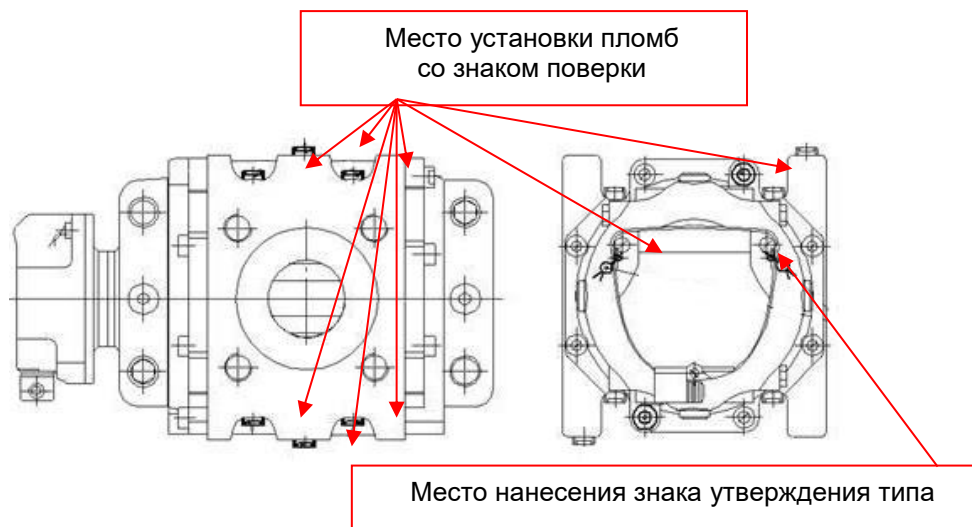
Схема установки пломб со знаком поверки и места нанесения знака утверждения типа на счетчики базового исполнения и Silver DN50, DN80, DN100, DN150.
